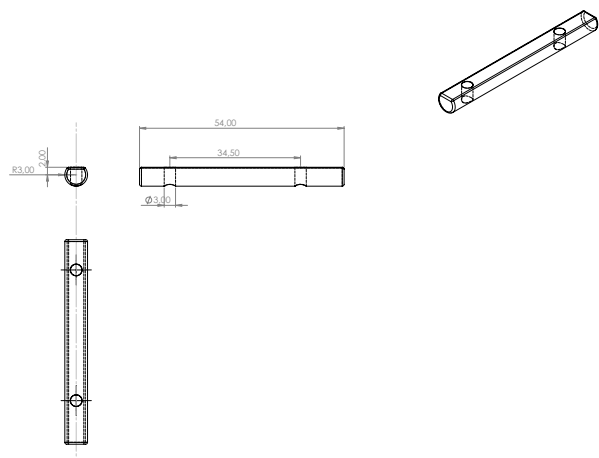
Desenho técnico - *String tree* para Braço Vidro.
